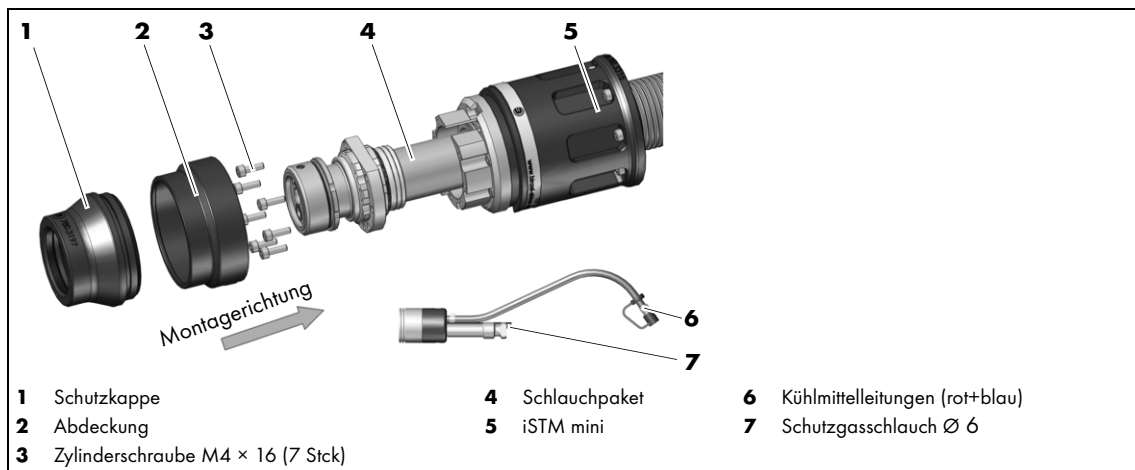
Schlauchpaket montieren iSTM mini für ABIROB® W
